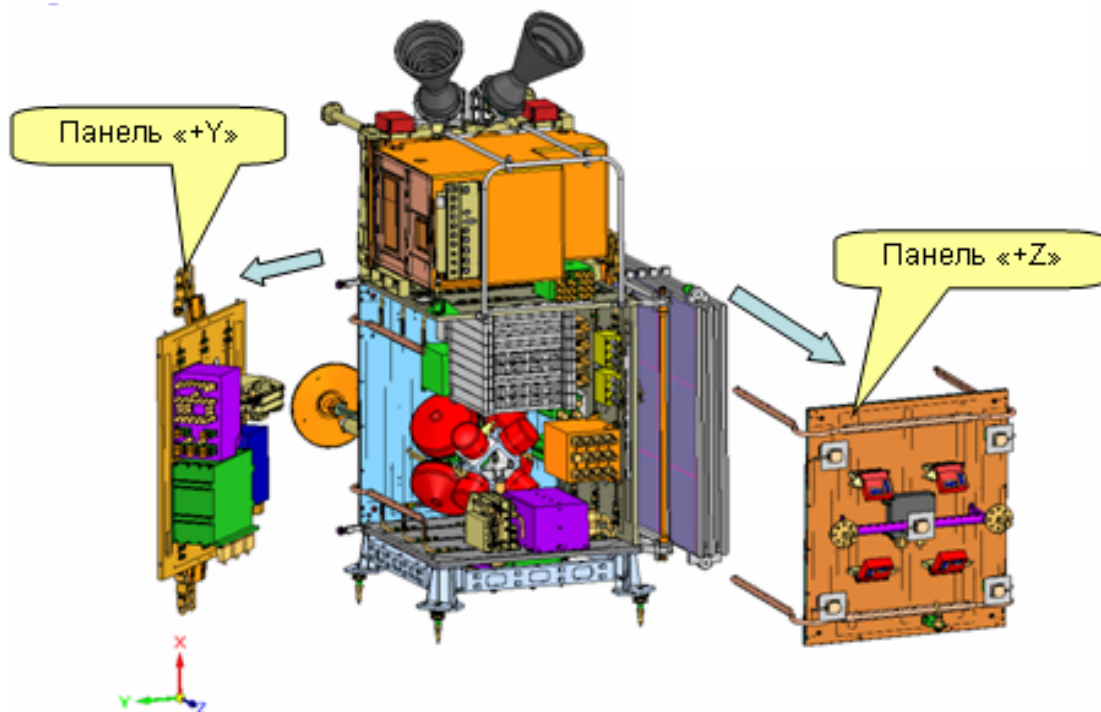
Общий вид компоновки блоков внутри модуля космической платформы КА
